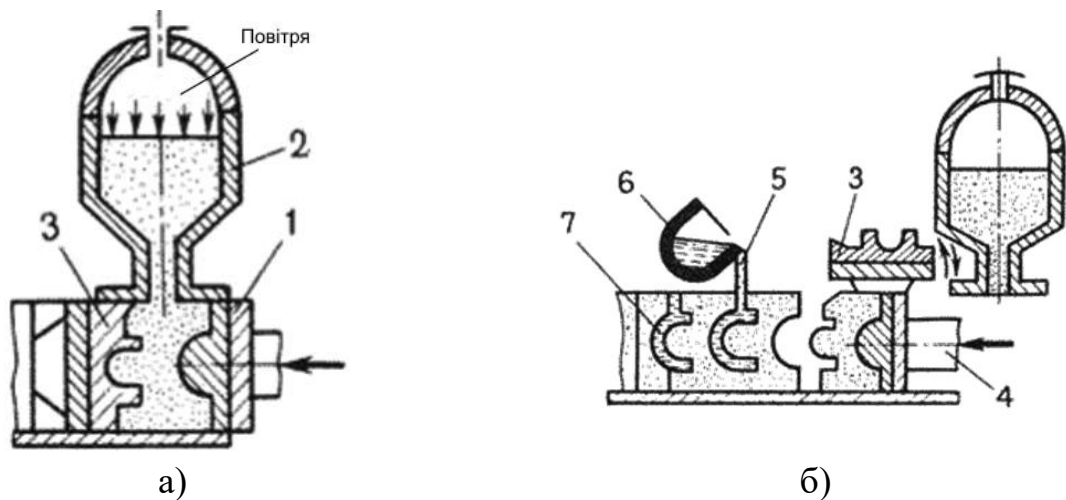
Схема виготовлення безопочних ливарних форм
